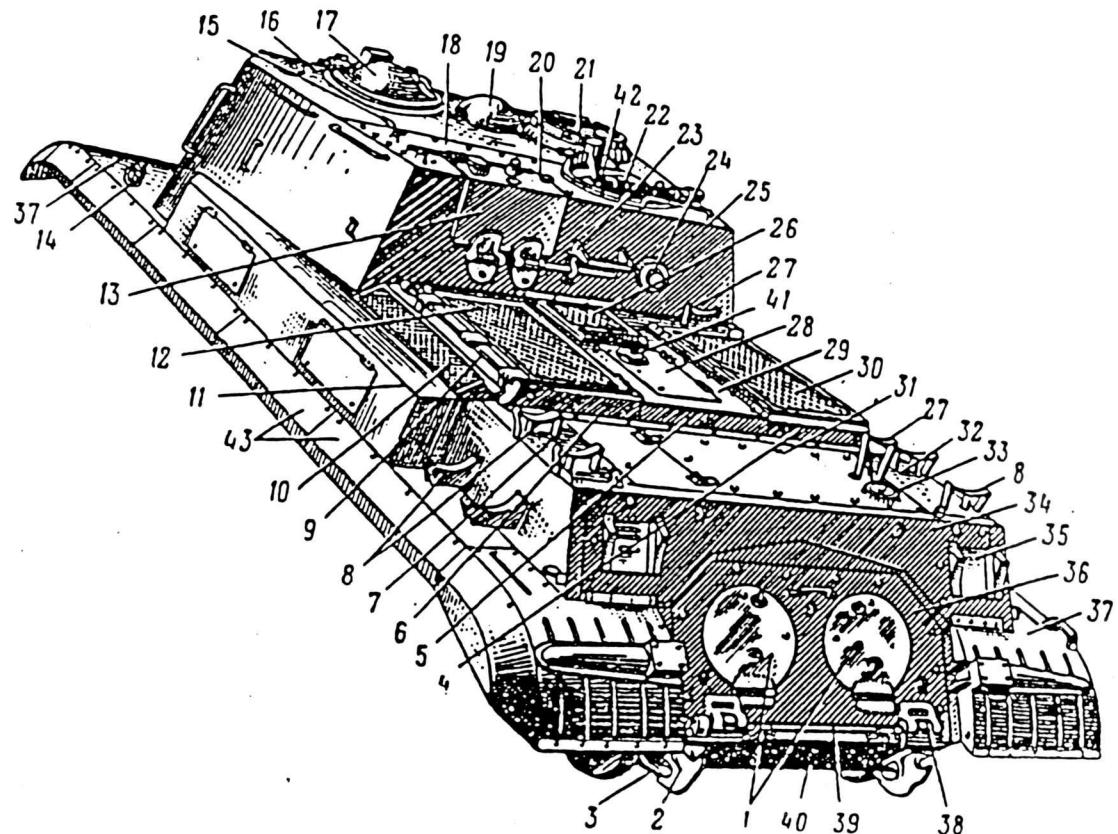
Общий вид корпуса (кормовая часть и крыша):
